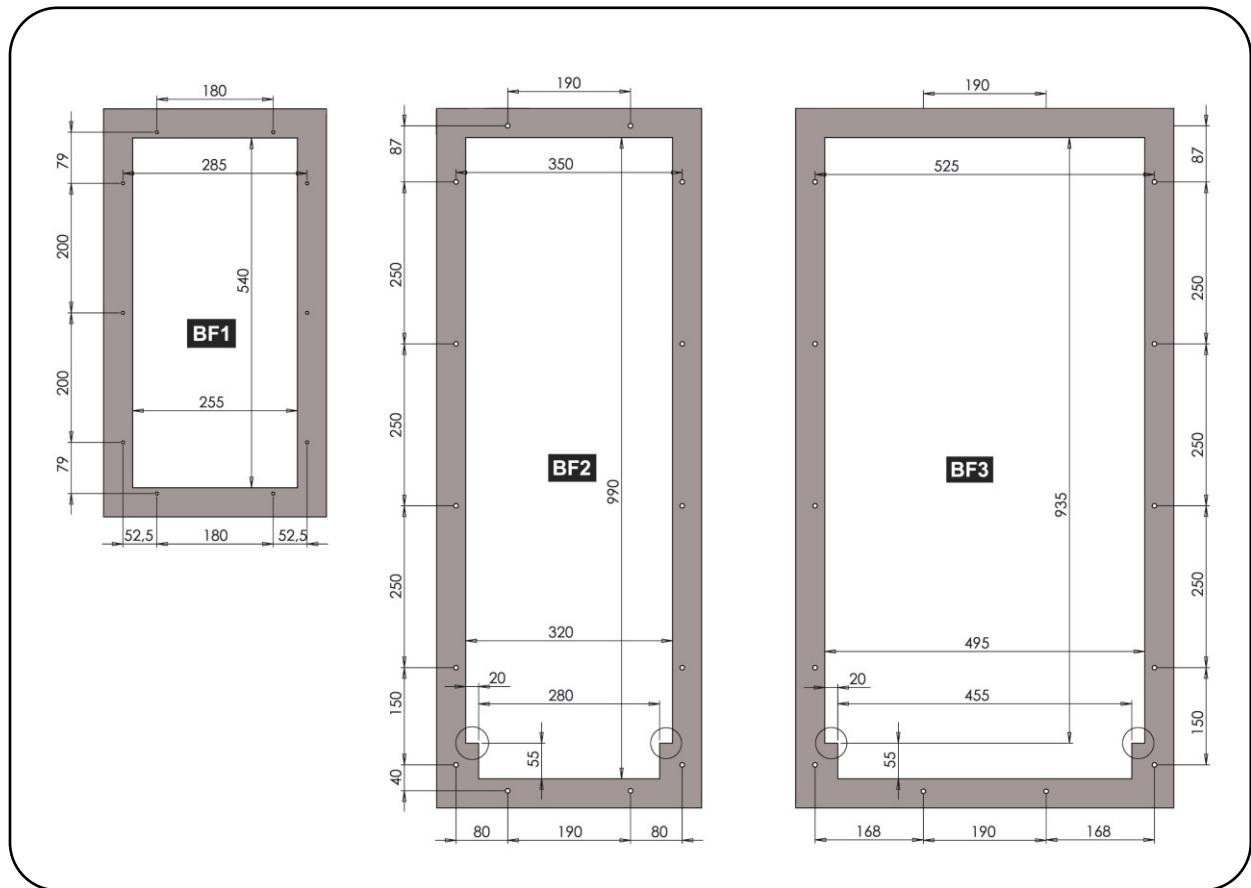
Dimensioni staffe di fissaggio a retro quadro / Rear panel brackets sizes
